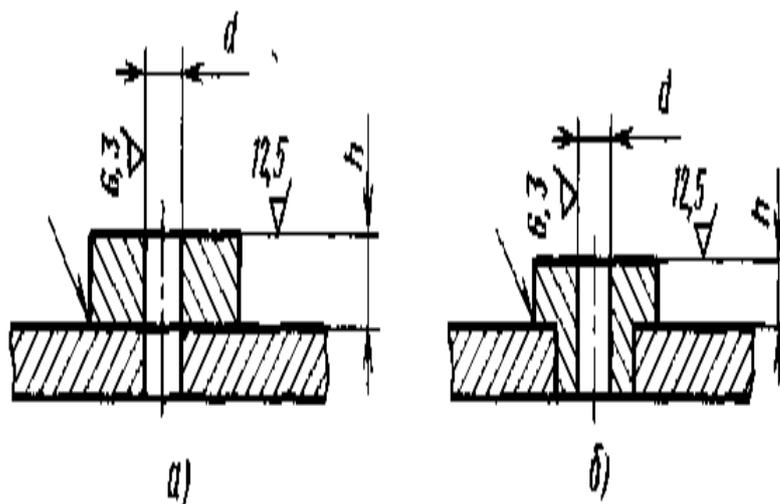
Сварные соединения втулок и бобышек с плоскими деталями
